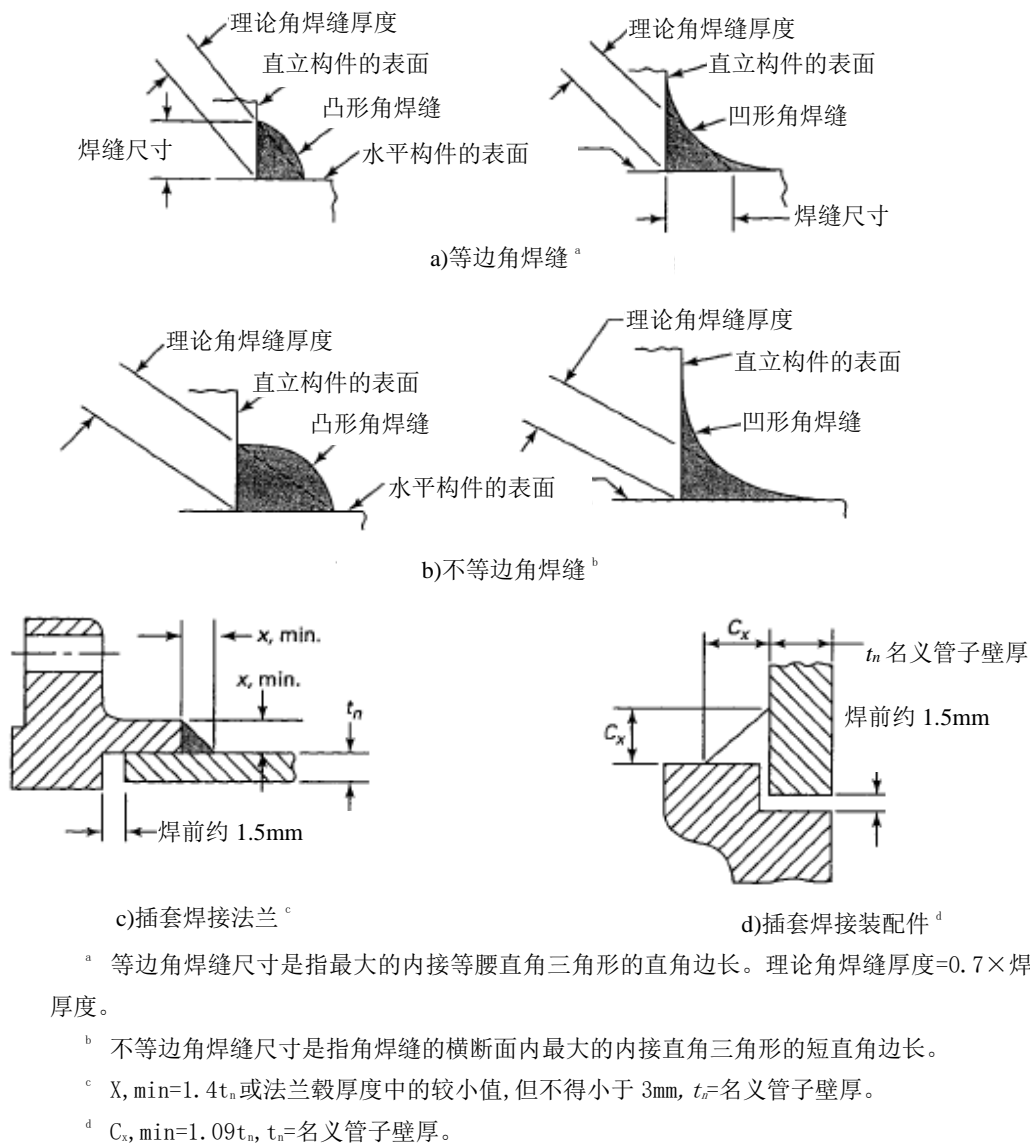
角焊缝、插套焊缝的尺寸和详图(对插套焊接管道尺寸的限制见 6.6.6.1.2)
